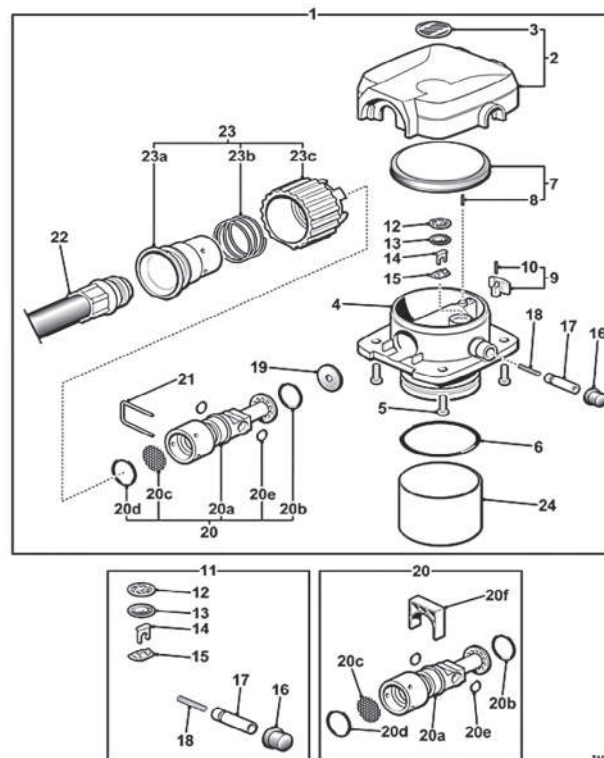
а) Вентиль K44-43.0-S140 – с конической резьбой;
